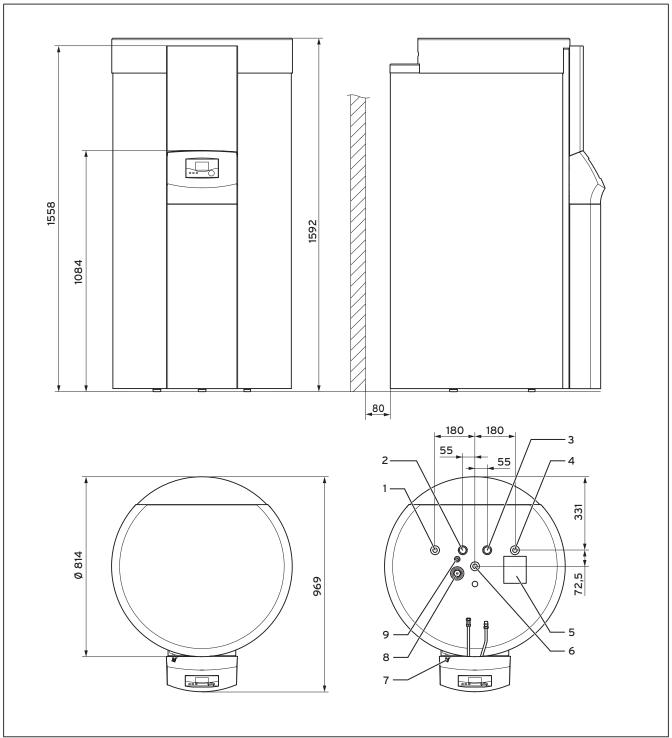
Размеры аппарата и патрубка водонагревателя гелиоустановки
